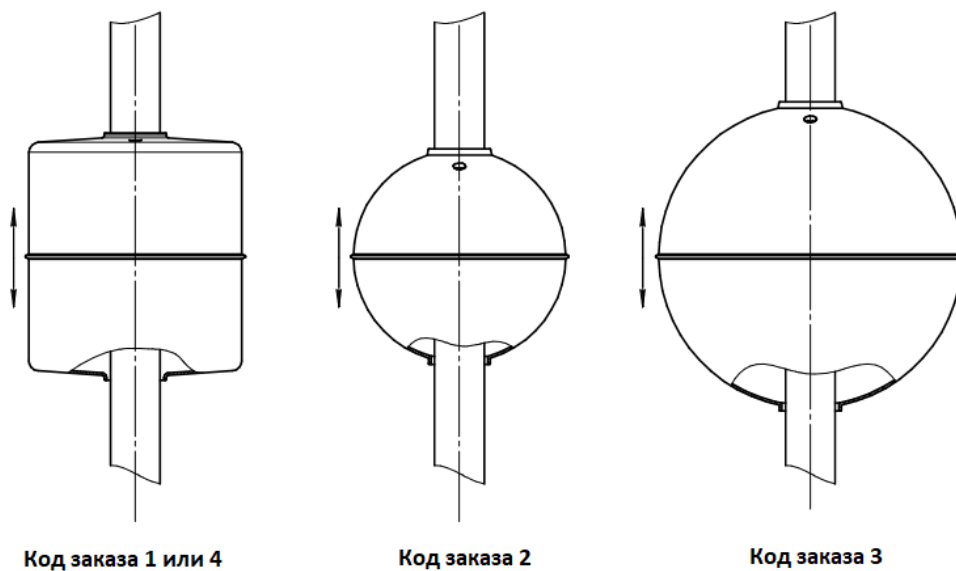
Монтажная часть ЭЛЕМЕР-УПП-11 с различными типами поплавков.
